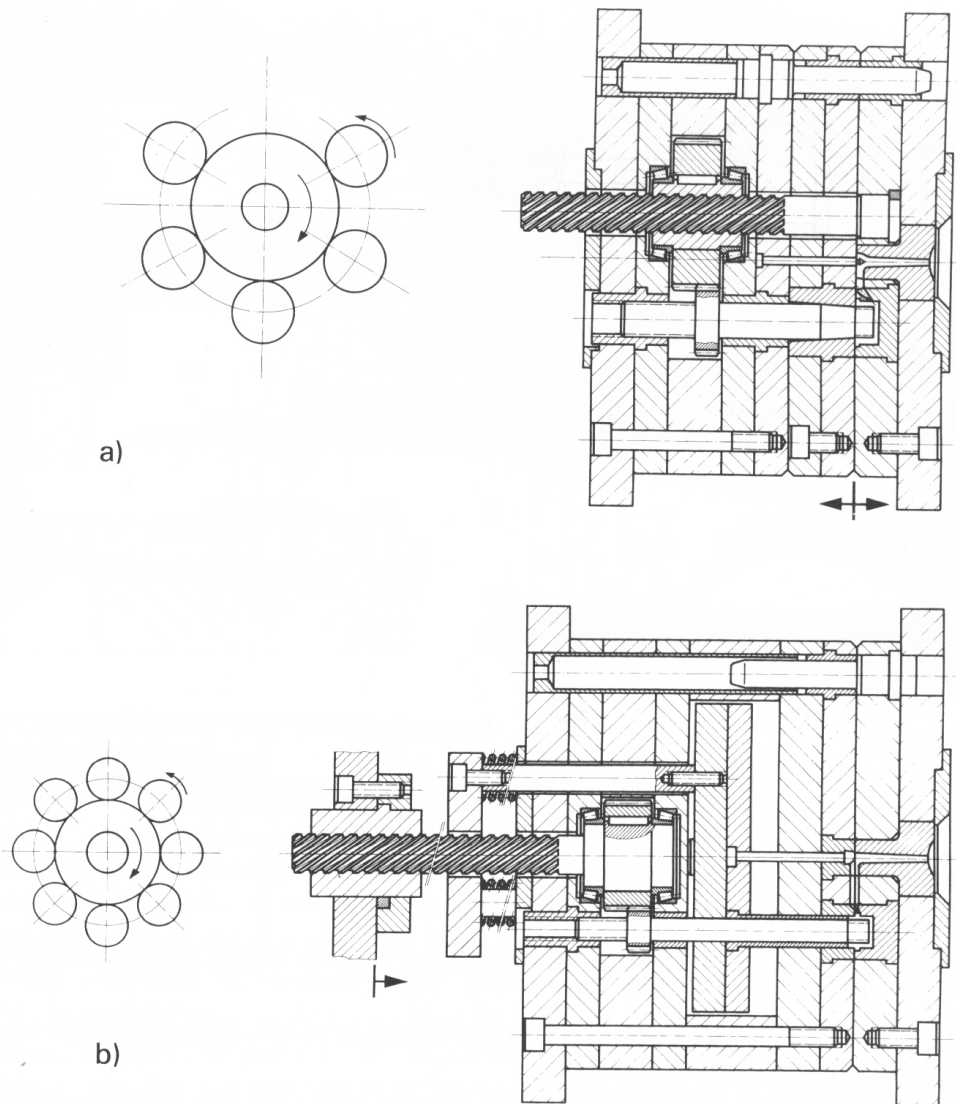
aplicaciones de mecanismos motrices de desenroscado (a) rotación accionada por el movimiento del molde (b) rotación accionada usando el eyector hidráulico de la maquina.
